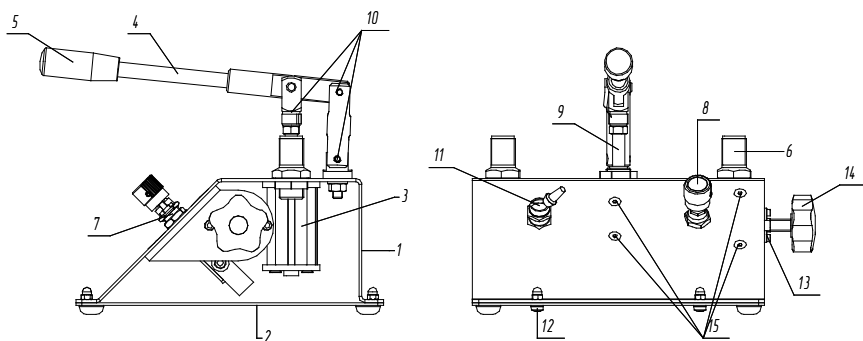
Пневматическое устройство для сравнительной калибровки:
